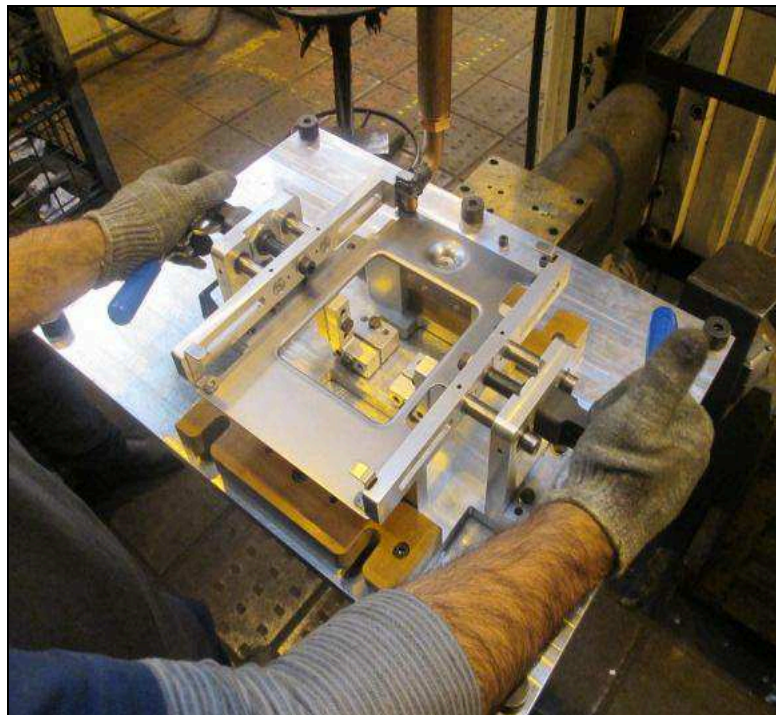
Operador ajustando as 4 chapas (item 3) para a soldagem na chapa 1.
